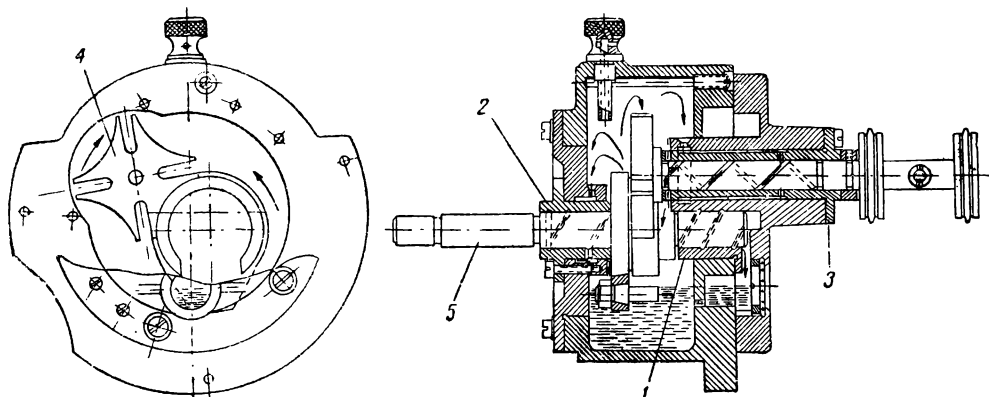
Опытный мальтийский механизм, испытанный на кинопроекторе типа К: 1 и 2 — подшипники эксцентрика; 3 — подшипник мальтийского креста; 4 — мальтийский крест; 5 — эксцентрик с пальцем
